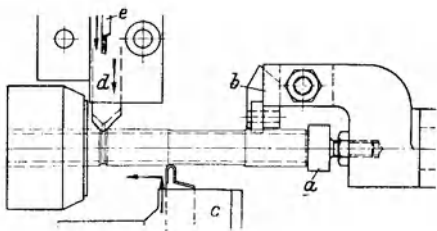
Bearbeitung eines Hohlbolzens aus Rohr.
